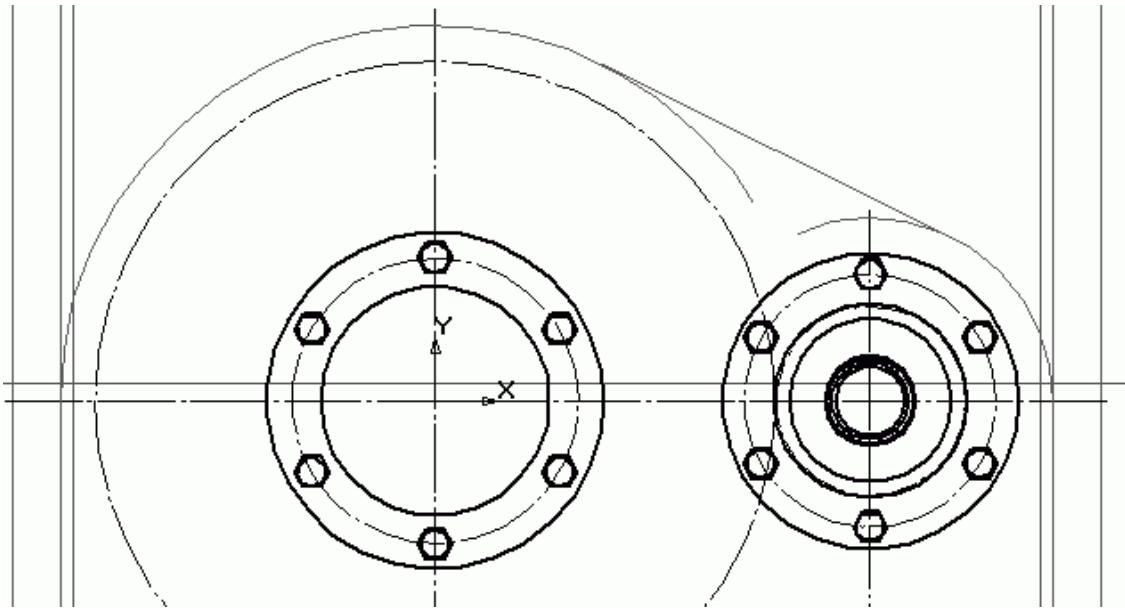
Сетка вспомогательных линий для построения крышки редуктора
